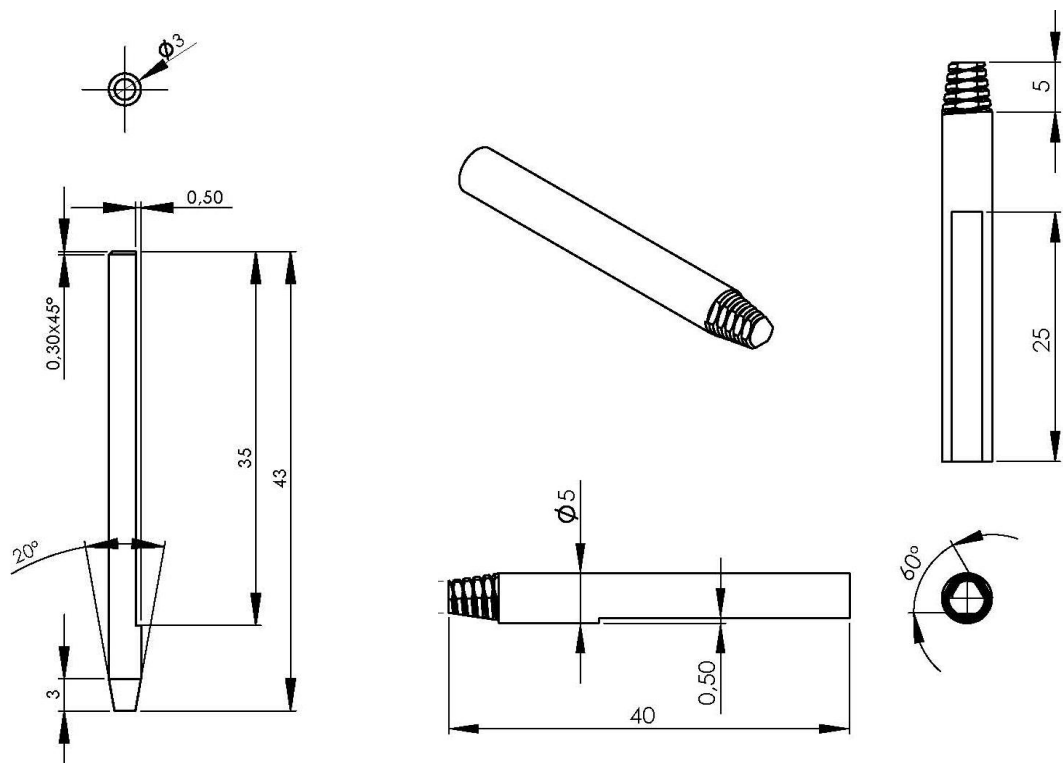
Technische Zeichnung der Werkzeugstifte Werkzeug 1 (links) und 2 (rechts)
